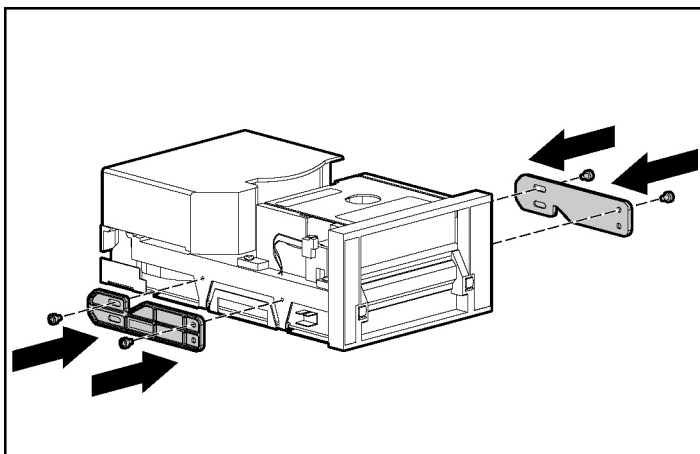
Befestigen der Schienen vom Blindmodul des Schachts für Wechselmedienlaufwerke an einem SCSI- oder IDE-Gerät
